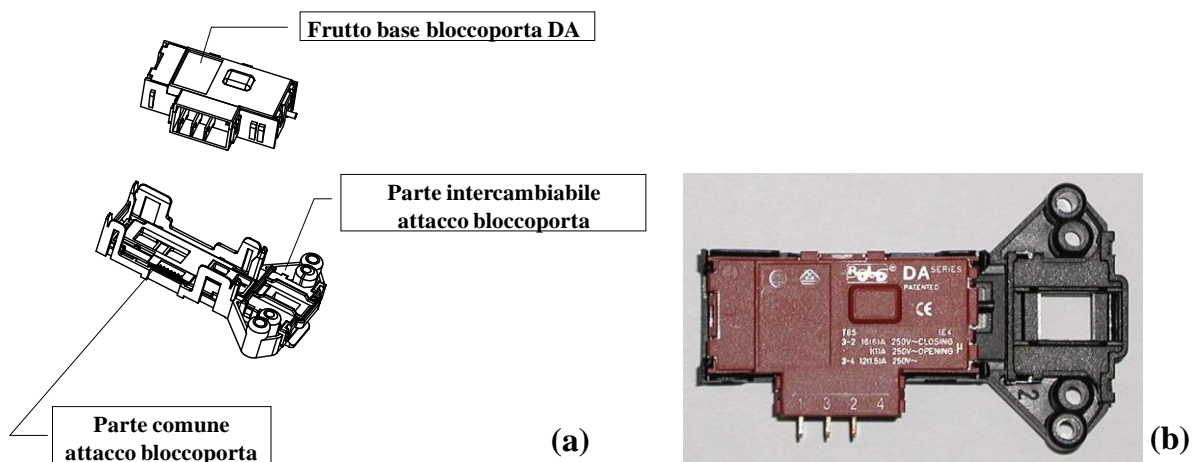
spezzato(a) e assembly (b) del bloccoporta DA.
